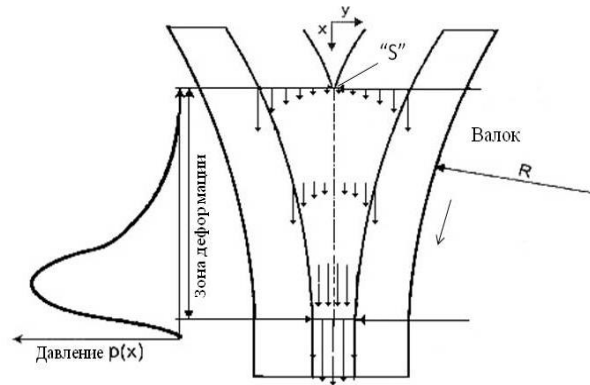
Схема сечения межвалкового пространства при прохождении жидкого металла в процессе валковой разливки-прокатки
